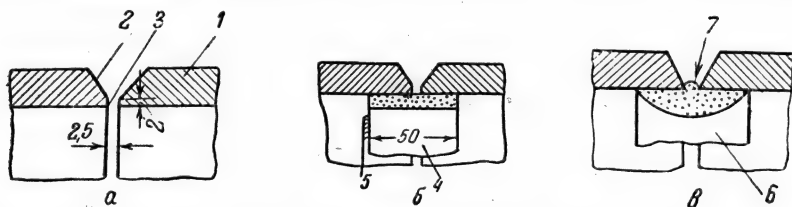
Типы сварных соединений: а — сварной V-образный стык; б — сварной стык с цилиндрическим подкладным кольцом; в — сварной стык с фасонным подкладным кольцом.
